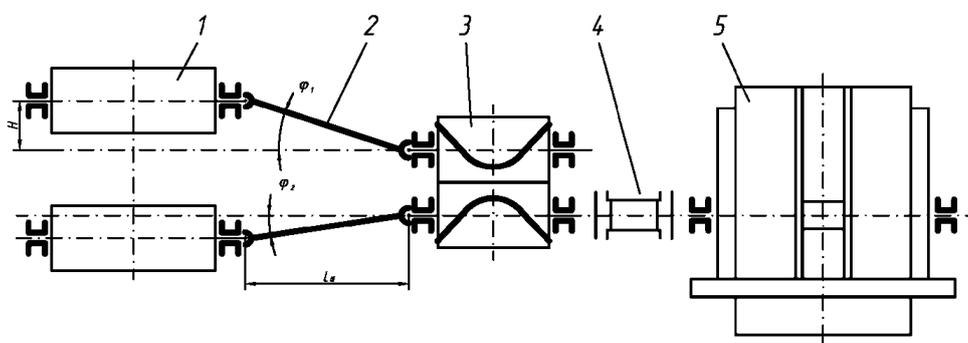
Схема установки универсальных шпинделей в рабочей линии стана: 1–рабочая клеть; 2–шпиндели; 3–шестеренная клеть; 4–муфта; 5–главный двигатель.
